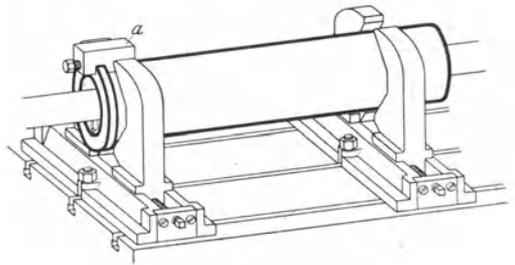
Spannen zylindrischer Hohlkörper mit 2 Zentrierschraubstöcken.
